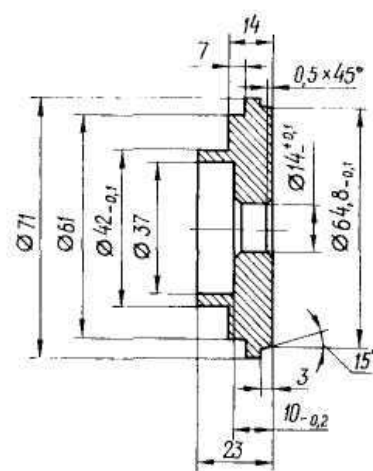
Оправка для запрессовки сальников и наружного подшипника ведомого вала колёсного редуктора
